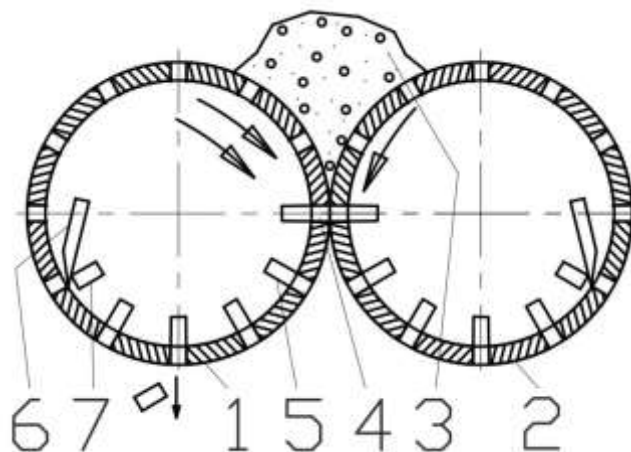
Схема двувальцевої дробарки.
